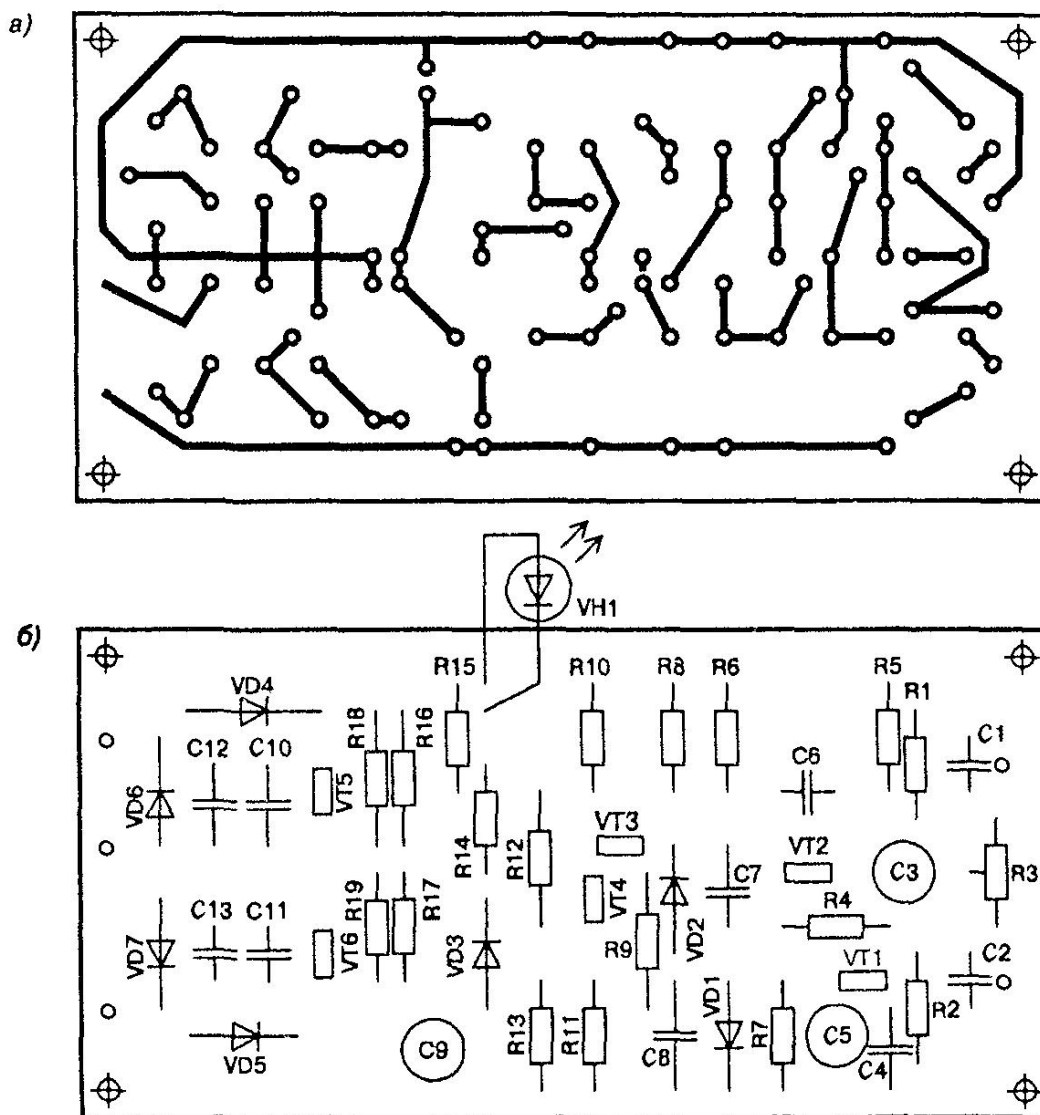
Печатная плата (а) и сборочный чертеж (б) шумоподавителя
